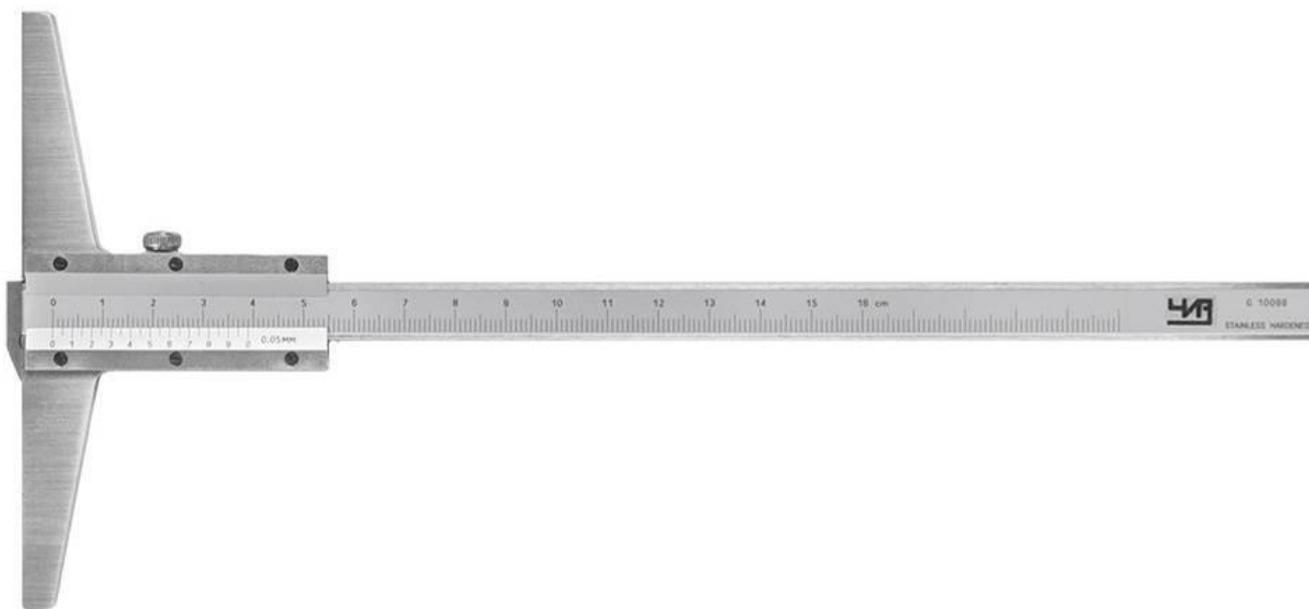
Общий вид штангенглубиномеров модификации ШГ с поперечным выступом штанги
